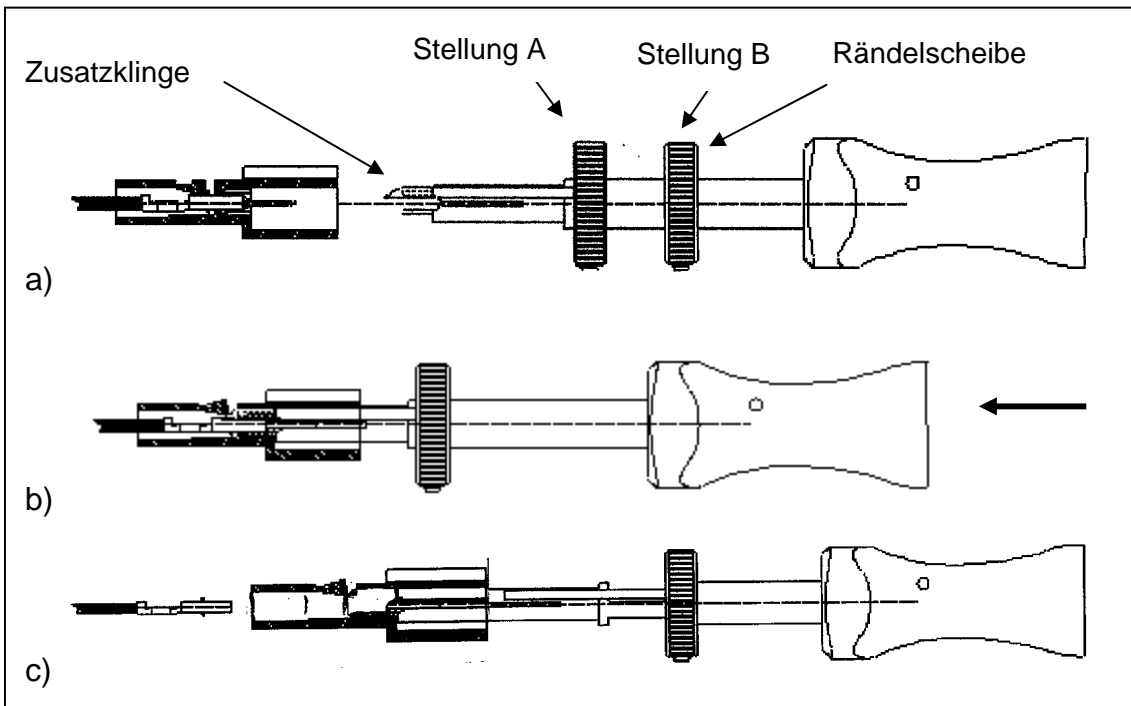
Entriegelung mit Werkzeug 2 72 00 54405 0
